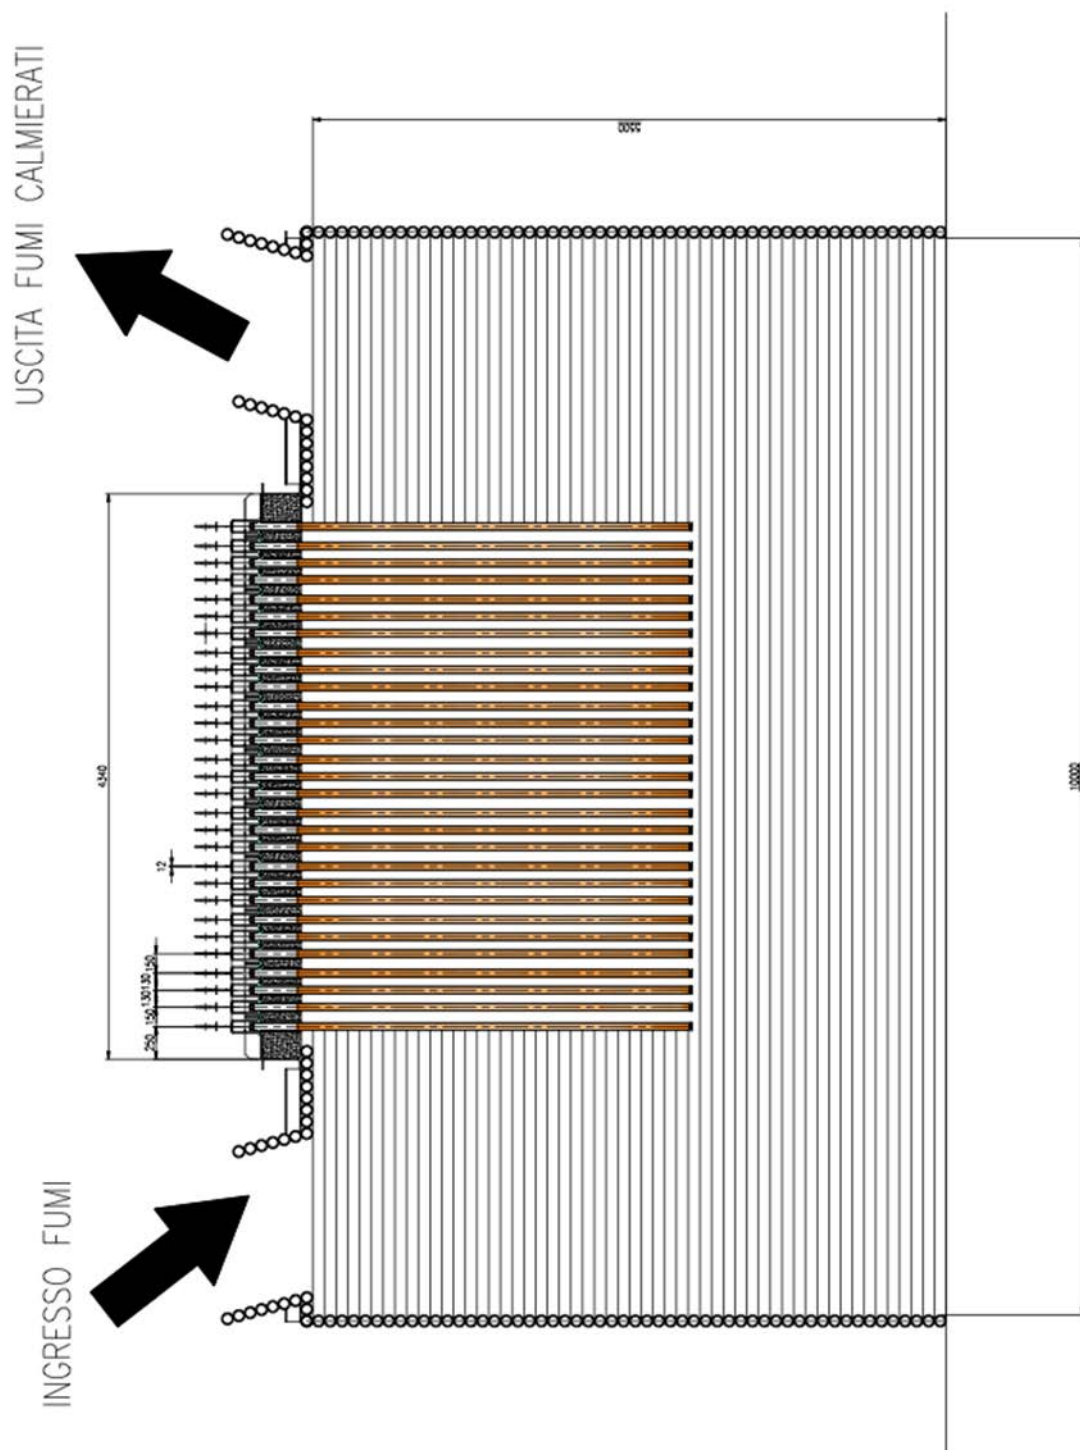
Vista frontale dei tubi all'interno della settling chamber e dimensioni della struttura di supporto.
